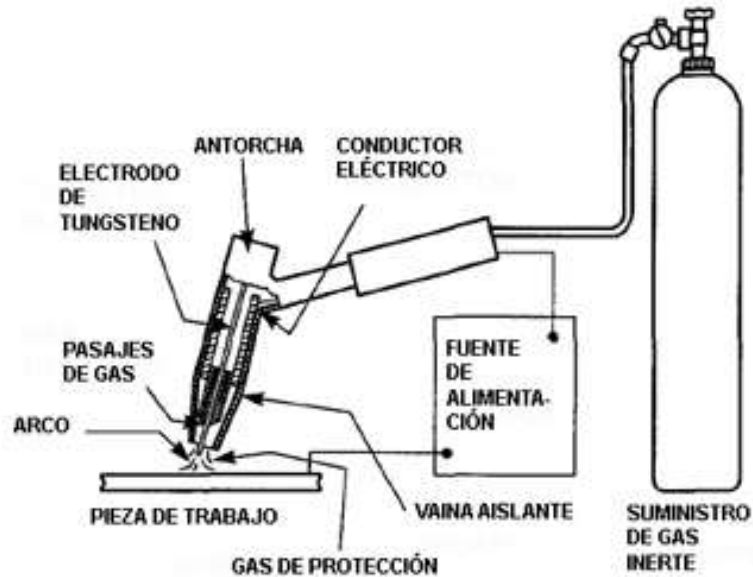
esquema de soldadura TIG, fuente: sapiensman.com
